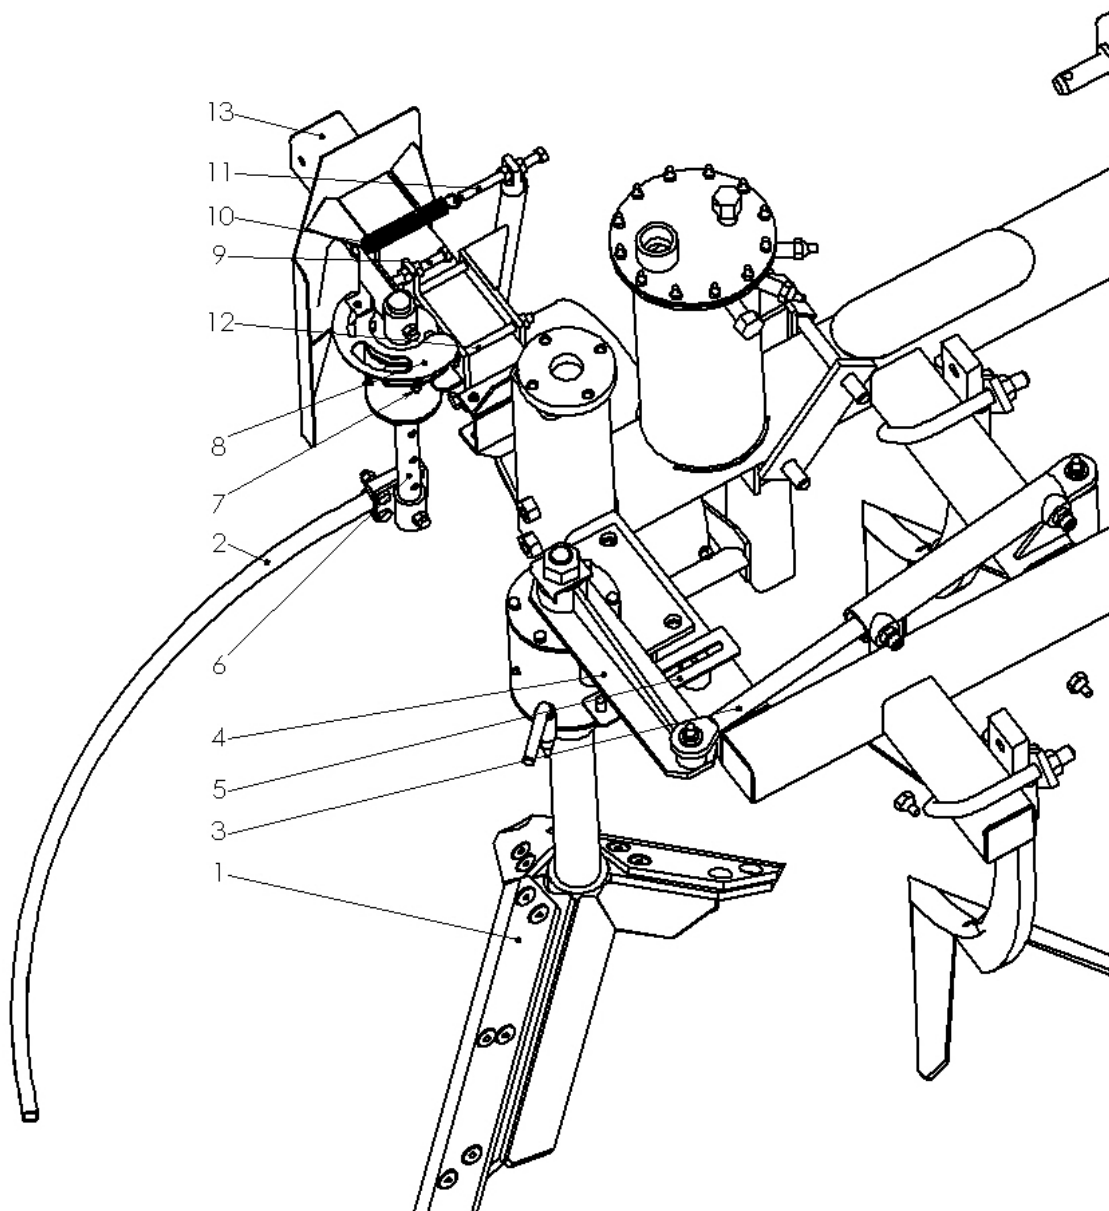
Регулировки щупа: 1 – поворотная лапа; 2 – щуп; 3 – гидроцилиндр поворотной лапы; 4 – рычаг поворотной лапы; 5 – кронштейн с датчиком №2; 6 – шток щупа; 7 - кронштейн с датчиком №1; 8 – флажок щупа; 9 – упорный винт начального положения щупа; 10 – пружина щупа; 11 - регулировочный винт пружины; 12 – стяжной болт механизма щупа; 13 – кронштейн механизма щупа
